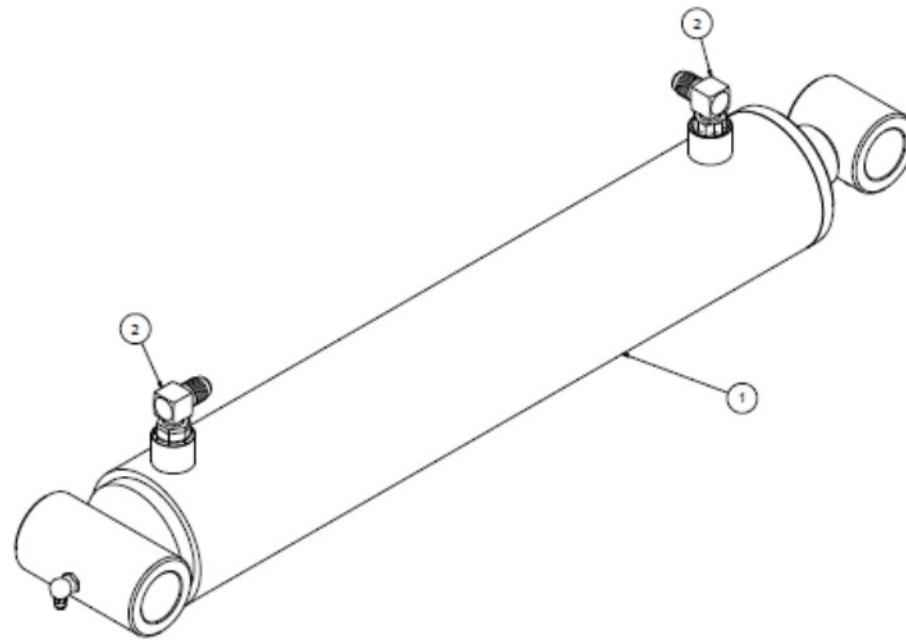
Чертеж гидравлического цилиндра механизма опрокидывания тележки – 815839
